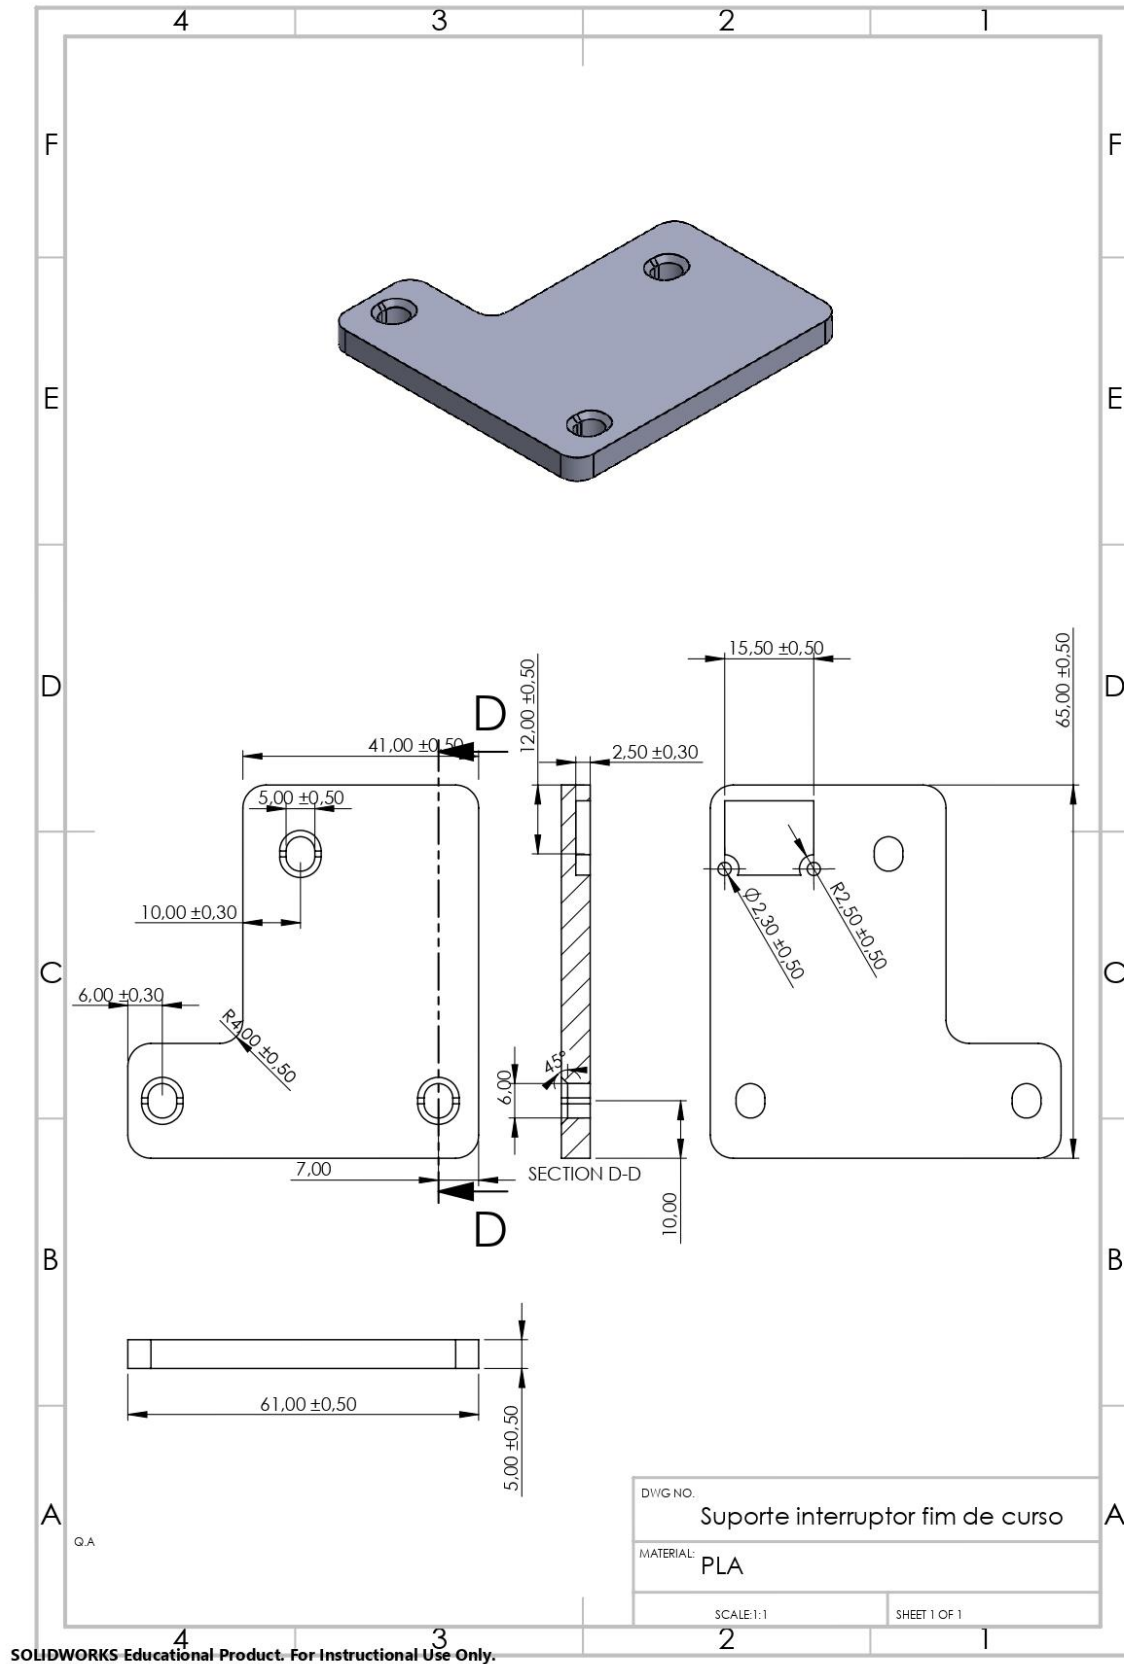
Desenho técnico do suporte do interruptor de fim de curso.
